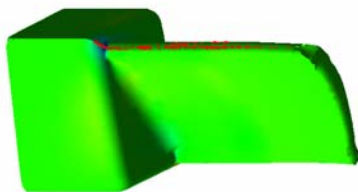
Видавлена заготовка компресорної лопатки, отримана з використанням комп'ютерного моделювання
